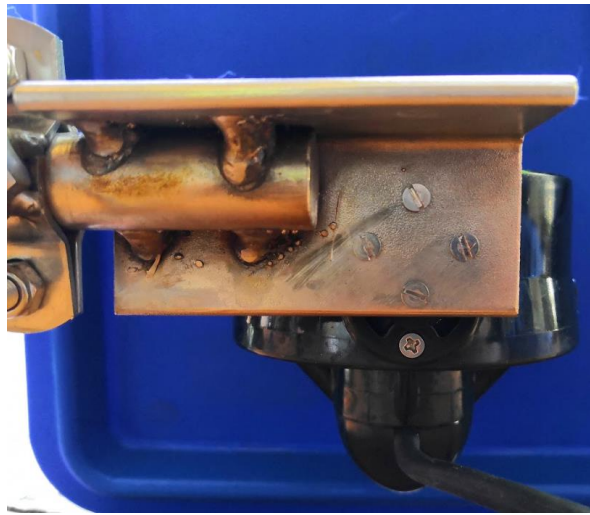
Soldadura de los perfiles y tornillos empleados
